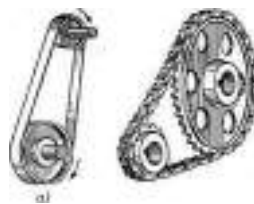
Передачи с гибкой связью: а — ременная; б — цепная
